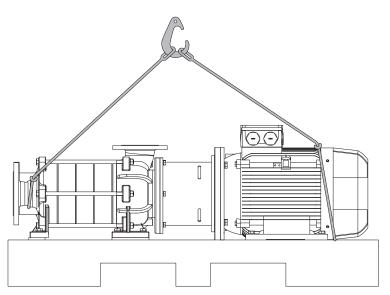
Pumpe mit Motor auf einer Grundplatte montiert
